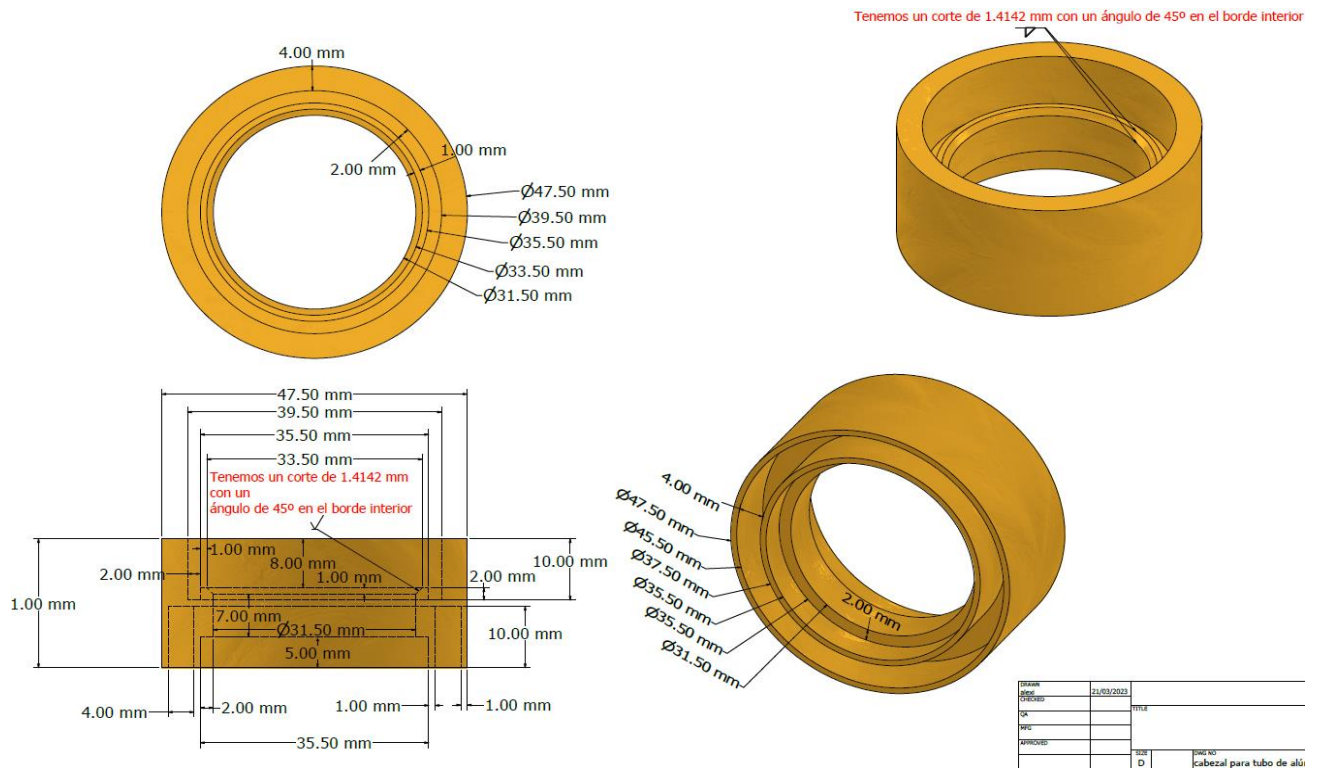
Pieza "D1" que ensambla con la pieza "C1".
